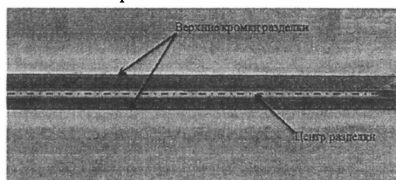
Обнаружение кромок и центра разделки стыка (до сварки)
